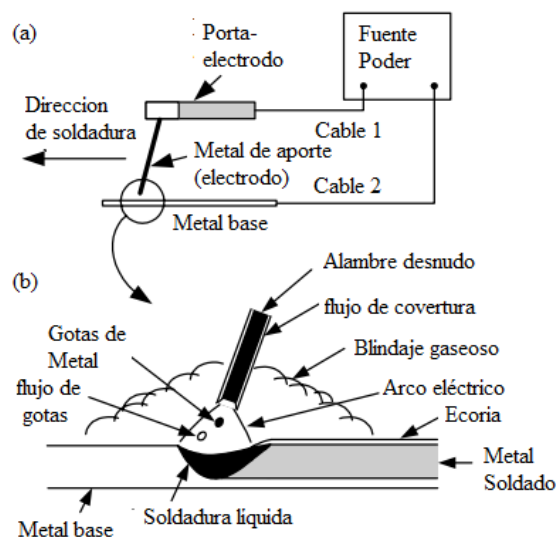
Soldadura blindada por arco eléctrico (a) proceso general, (b) área de soldado ampliada (Dourado, 2014).
